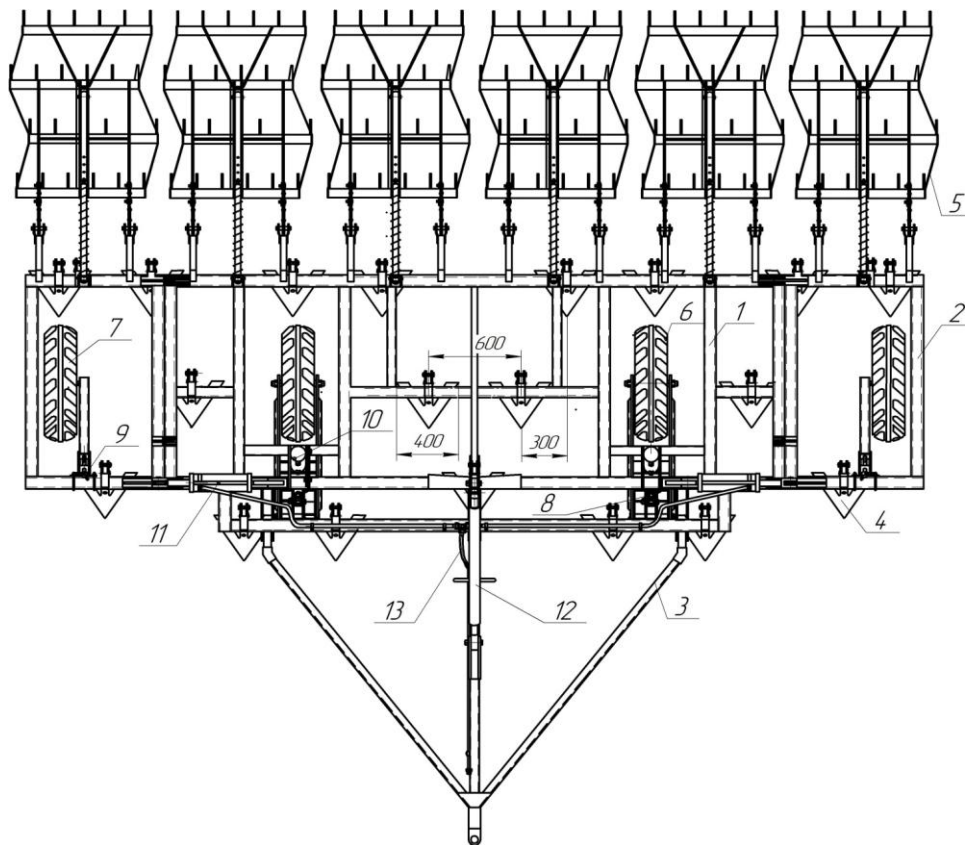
Схема універсального комбінованого культиватора КПМ-4-6: 1 – рама; 2 – секція; 3 - причіп; 4 – універсальні культиваторні лапи; 5 – борони зубові; 6 – опорні колеса центральної секції; 7 – опорні колеса бокових секцій; 8,9 – гвинтові механізми регулювання глибини обробітку; 10 – гідроциліндри переведення культиватора з робочого в транспортне положення; 11- гідроциліндри підіймання секцій; 12 – телескопічна тяга зміни положення причепу
